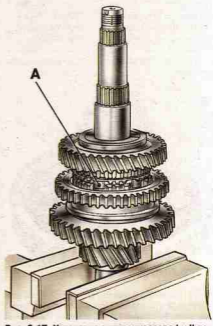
Установка синхронизатора I и II передач и ведомой шестерни II передачи
